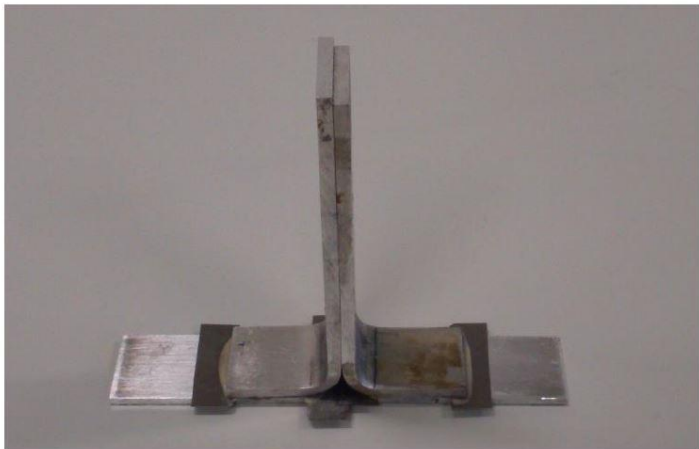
Exemplo de junta fabricada pelo autor [66].
